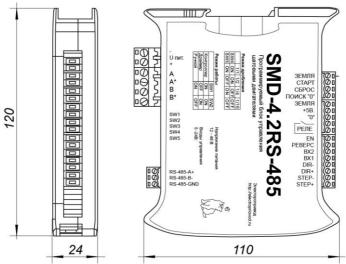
Габаритные размеры блока управления SMSD-4.2RS-485
